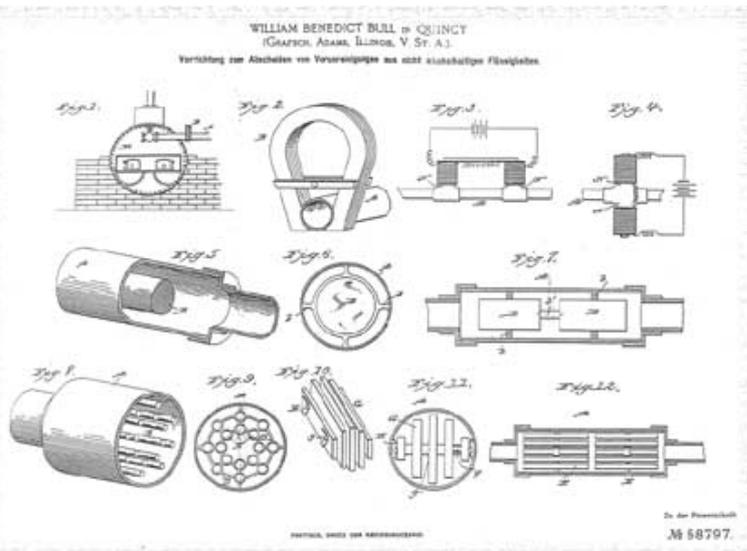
Fast alle erdenklichen Formen der Wasseraufbereitung, wie sie auch heute noch angewendet werden, wurden schon 1890 patentiert.
